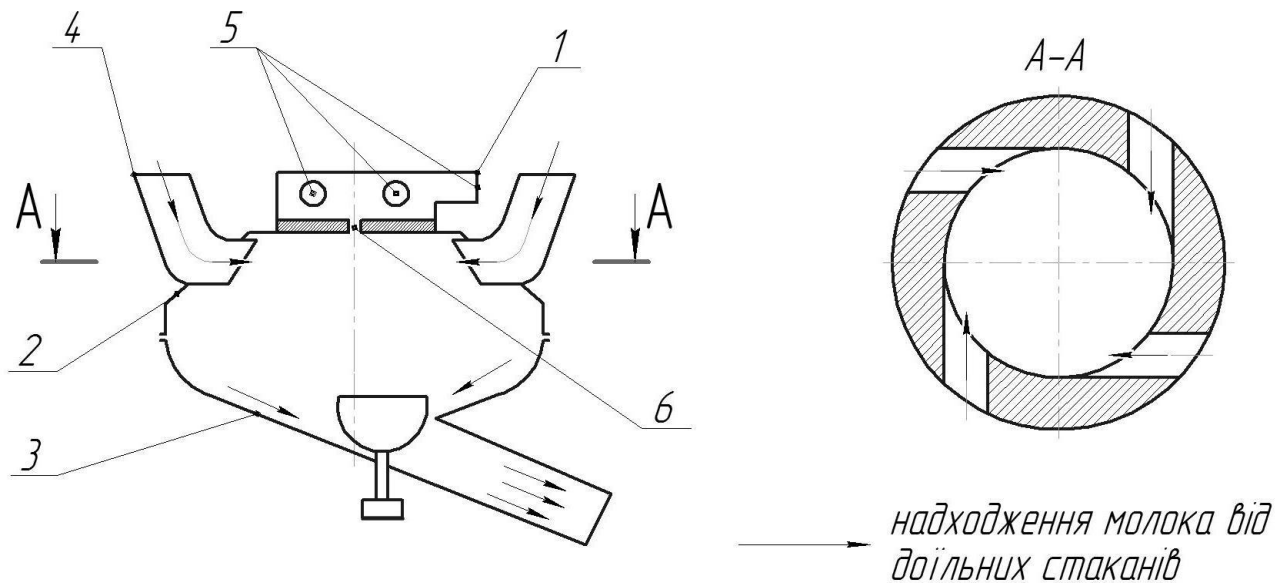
Схема конструкції розробленого колектора: 1 – камера розподілу змінного тиску; 2 – корпус колектора; 3 – камера для збирання молока; 4 – патрубки молочних трубок; 5 – патрубки камери розподілу змінного тиску; 6 – отвір сполучний [15]
